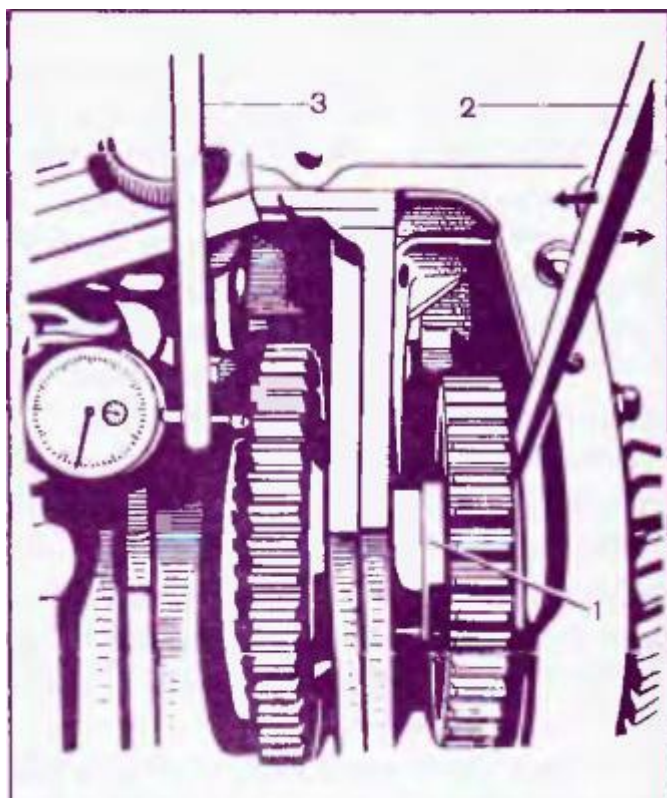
Проверка осевого зазора в подшипниках вторичного вала трактора МТЗ
